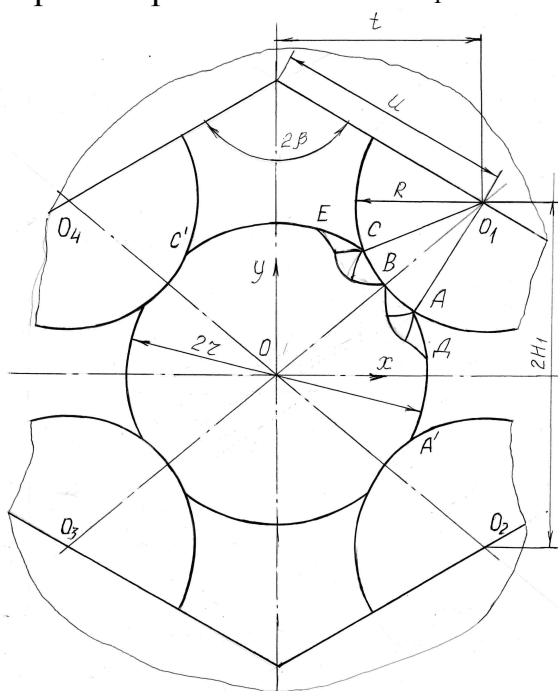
Схема обжатия круглой заготовки вырезными профилированными бойками
